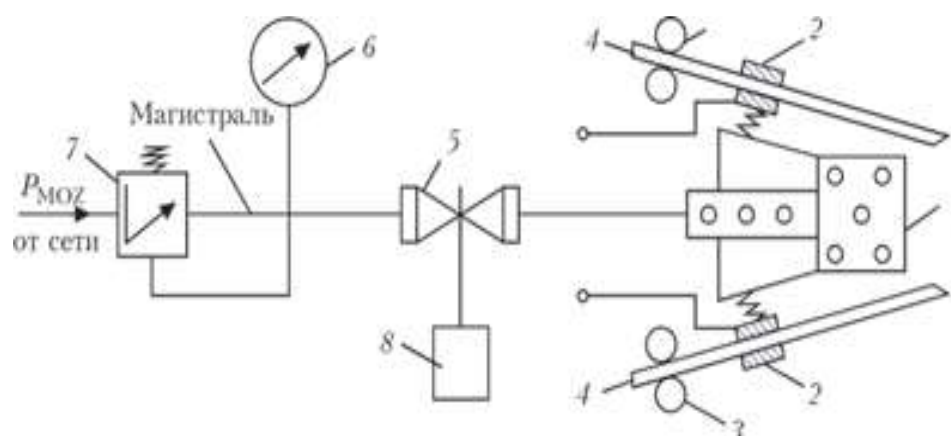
Схема головки для пульсирующего распыления: 1 – распыляющее сопло; 2 – токоподводы; 3 – ролики; 4 – электродный материал; 5 – пульсатор; 6 – манометр давления; 7 – редуктор давления; 8 – электродвигатель
